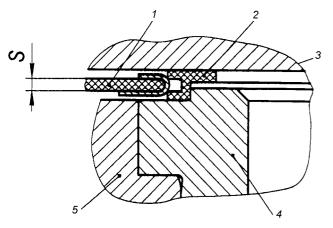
Газовый стык двигателей ЯМЗ с общей головкой (положение деталей перед затяжкой крепежа головки цилиндров):
